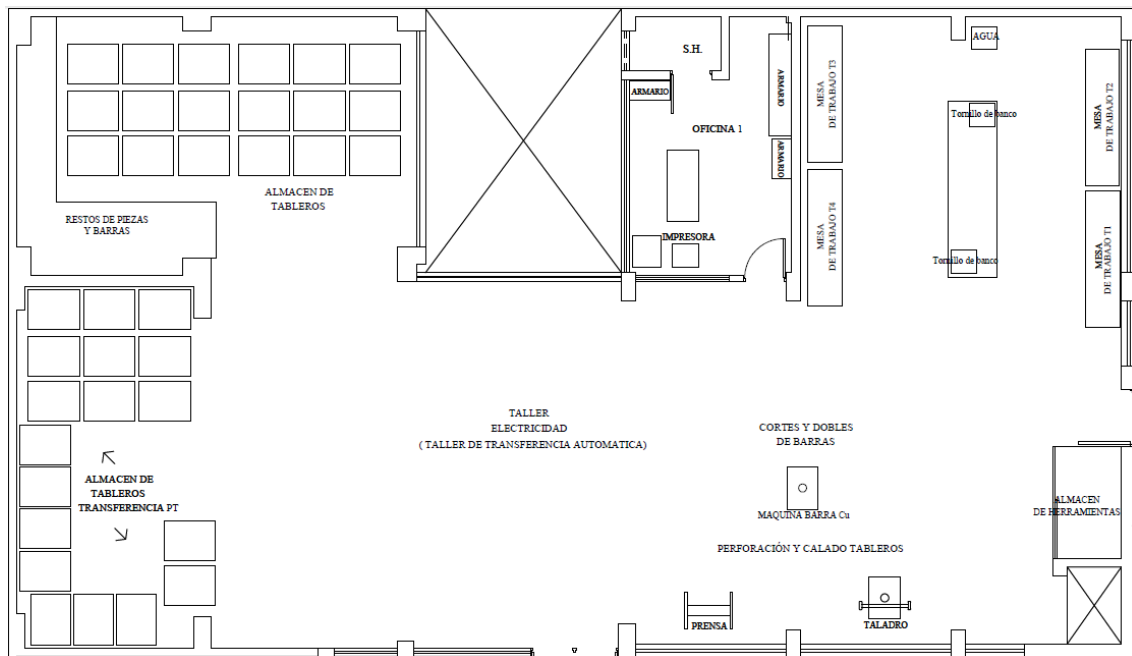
Distribución de planta fabricación de tableros de transferencia automática (nueva). Fuente: elaboración propia.
